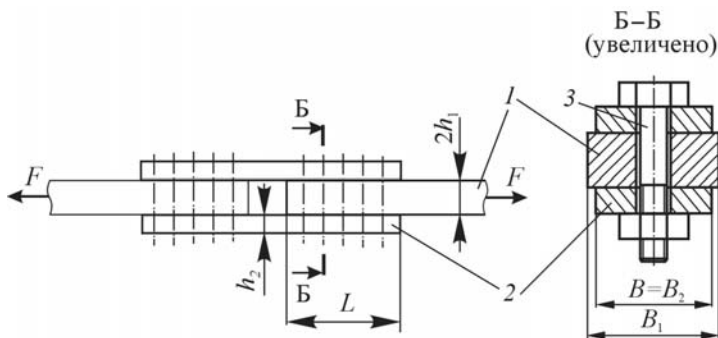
Резьбовое соединение, образованное пластиной и двумя накладками
